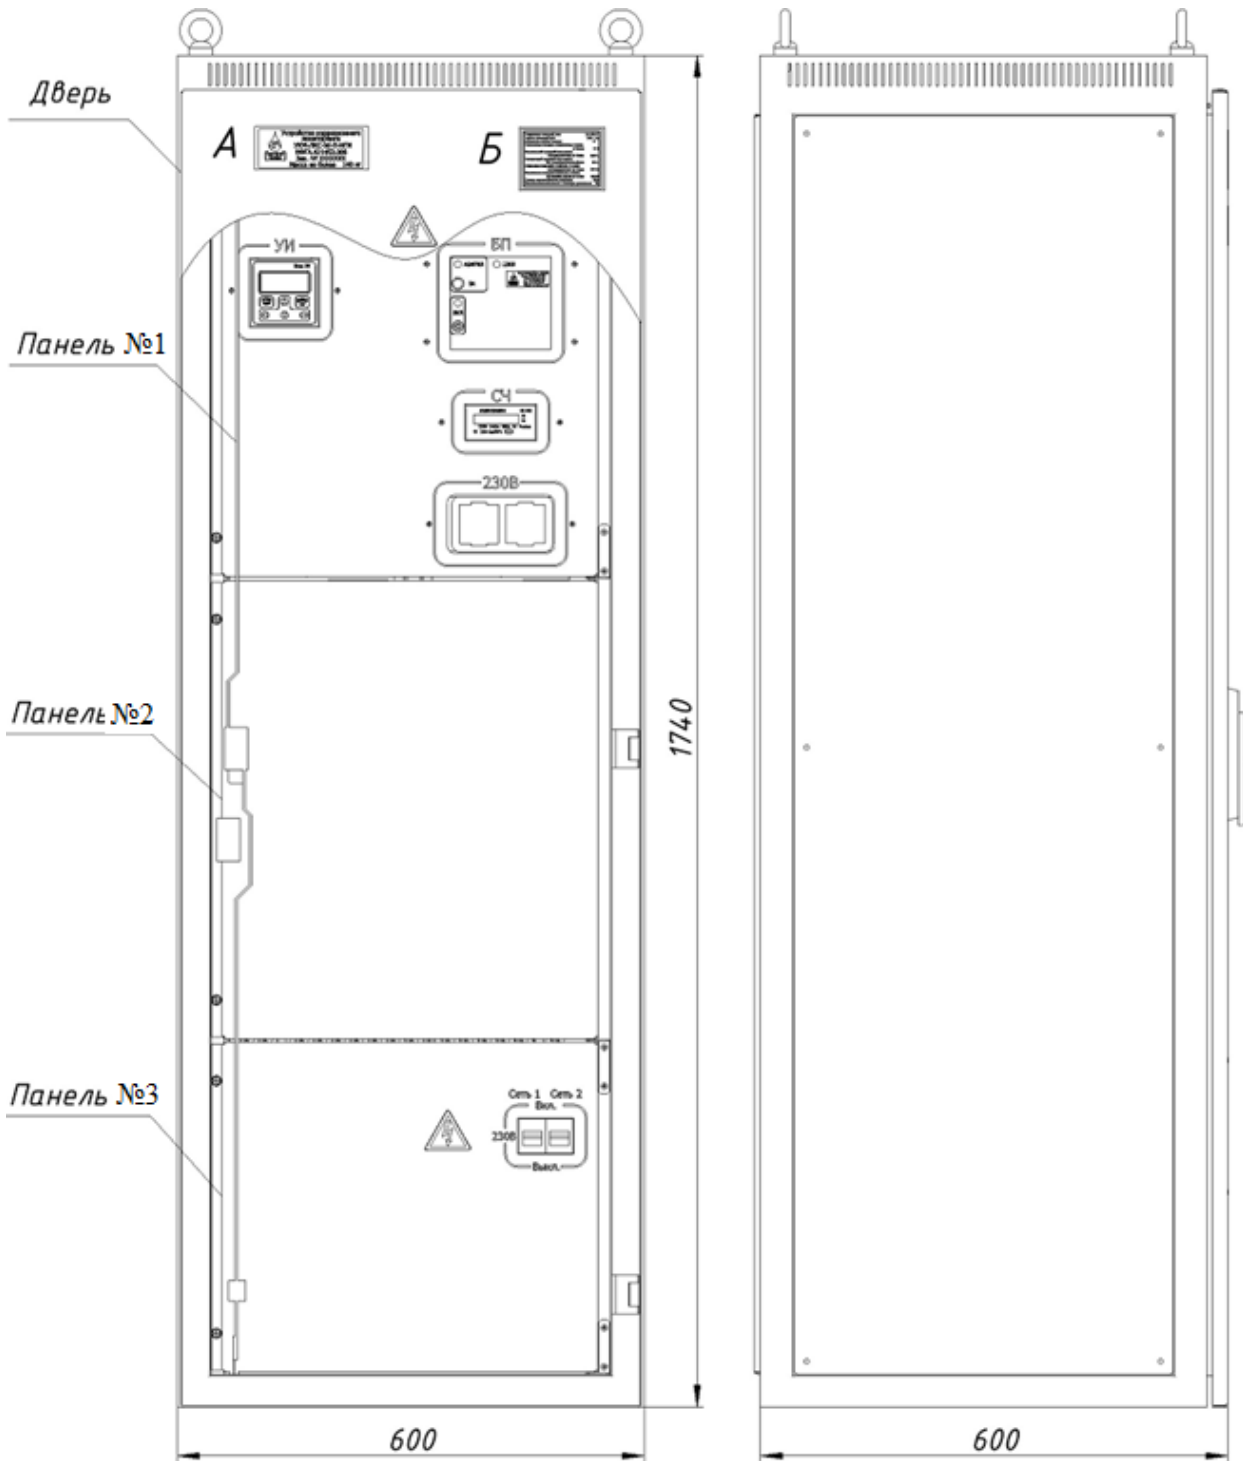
Габаритные размеры устройства УКМ-НГИ-ЛКС-06 (У2)
